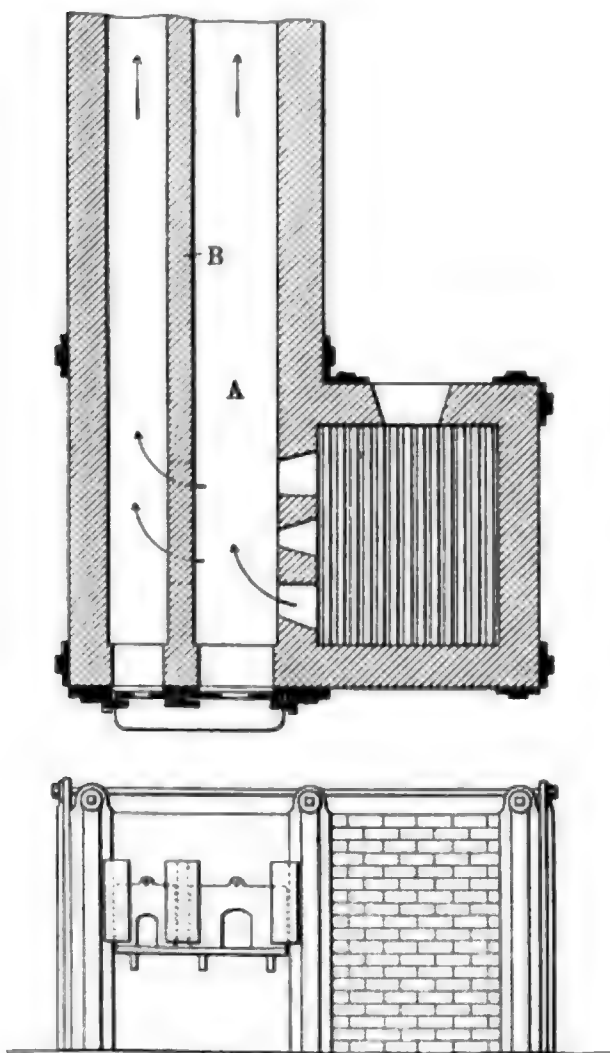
Rohrschweißofen mit Vorwärmer.
